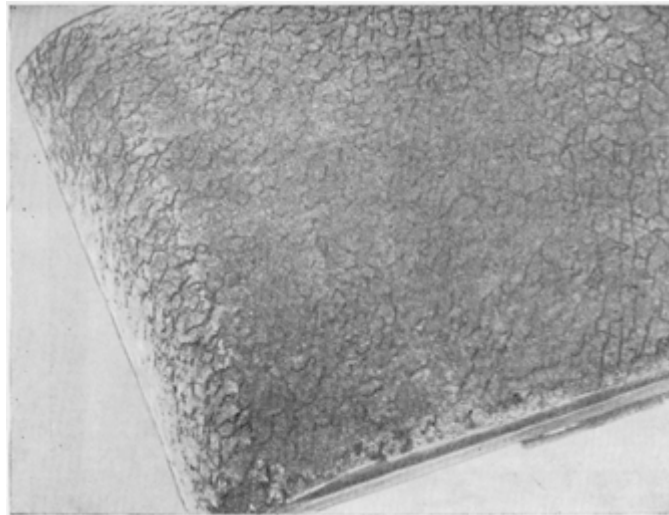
Внешний вид заготовки с чешуйчатостью
